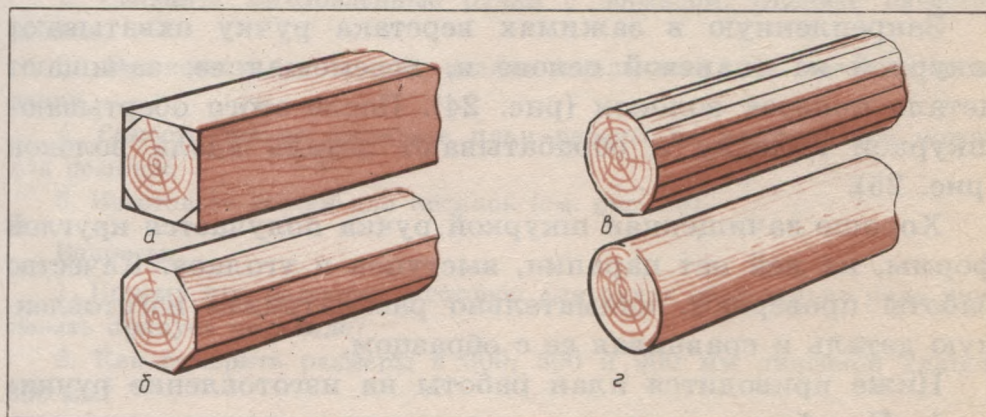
Скругление ручек носилок: а — разметка; б — строгание восьмиугольника; в — скругление углов; г — зачистка.
